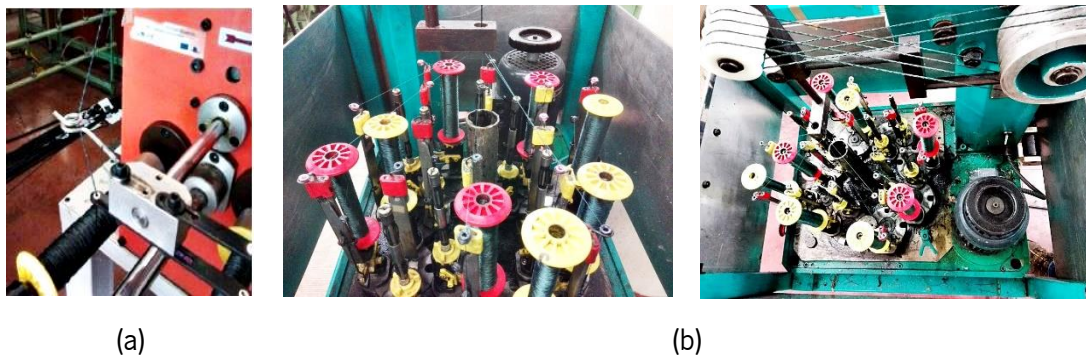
Bobinagem (a); Fabrico da rugosidade (b)
